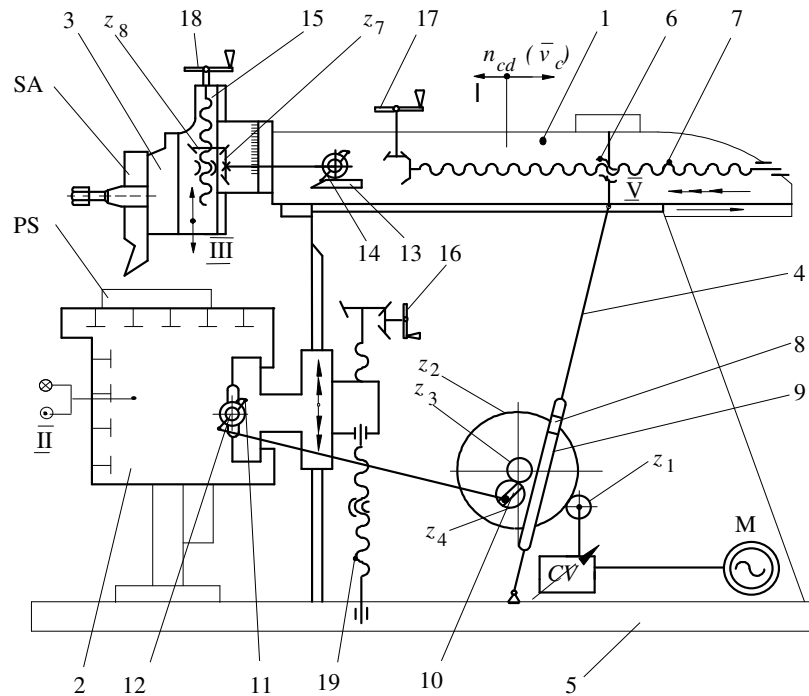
Schema de principiu a mașinii de rabotat cu cap mobil (șeping):
